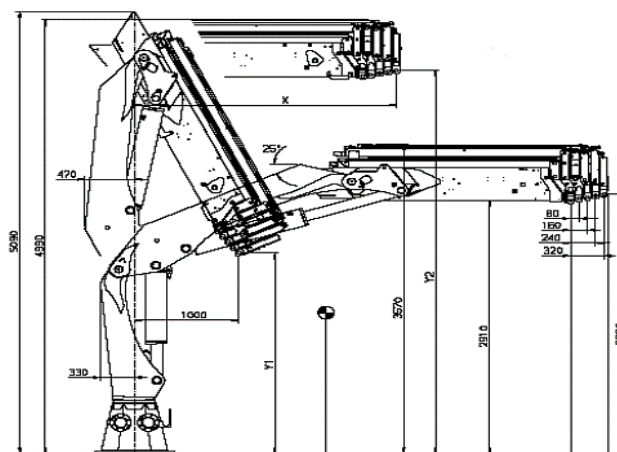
Grúa elevadora para la lancha rápida, ubicada en la cubierta principal.
